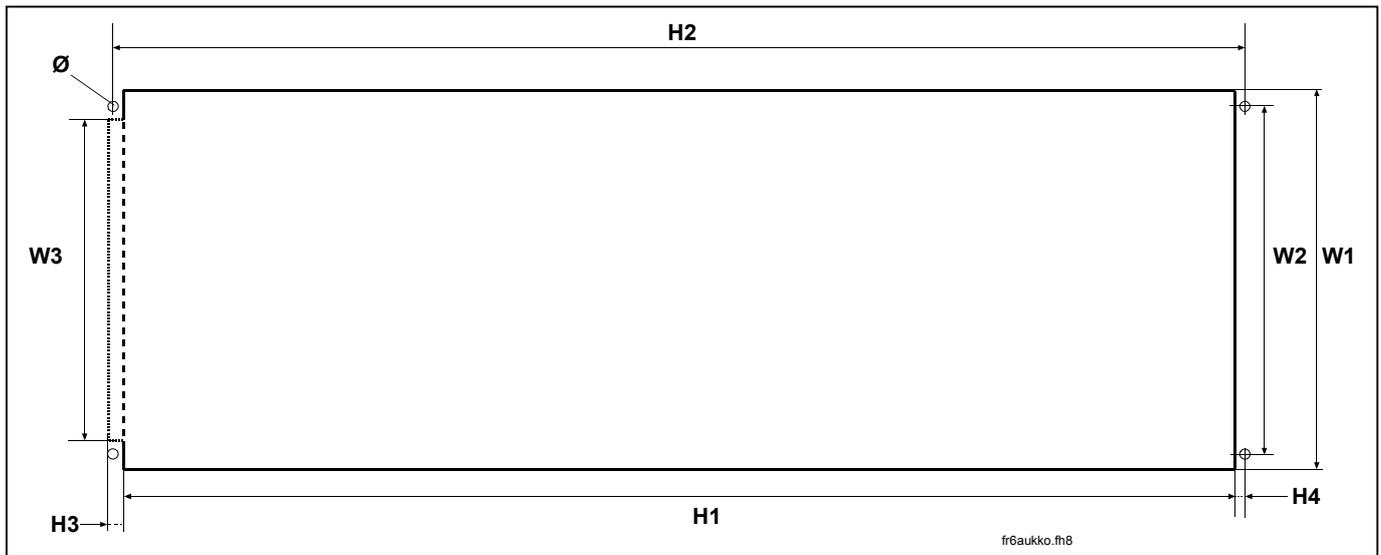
Установочные размеры для преобразователей частоты фланцевого исполнения, габариты с FR4 по FR6
